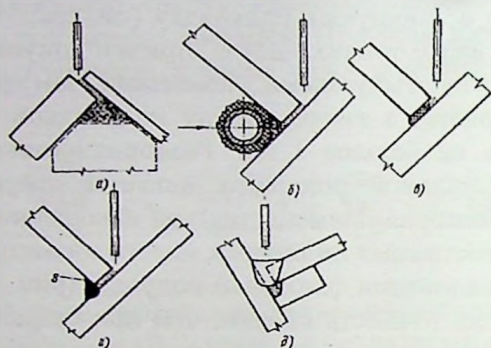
Схема способов сварки под флюсом угловых и тавровых швов:
